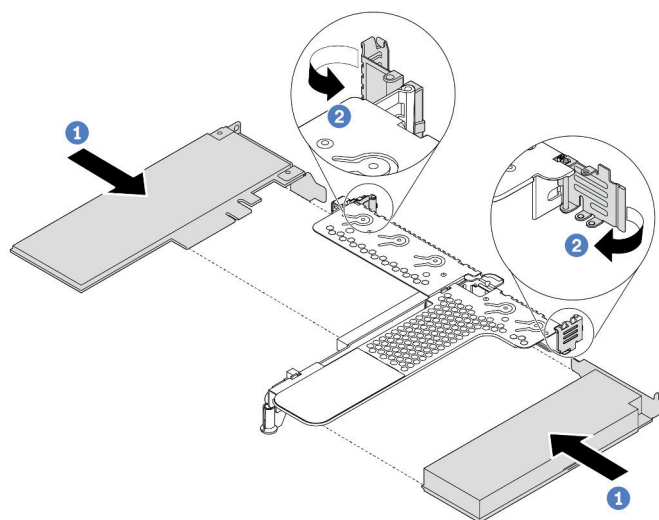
Instalação do adaptador PCIe no conjunto de placa riser LPFH
